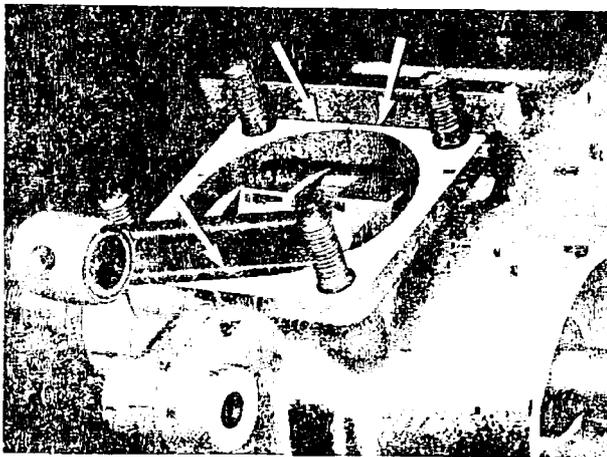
Der Pleuelschaft bzw. die Kurbelwelle müssen symmetrisch zur Gehäusetrennfuge liegen (unterer Pfeil). Die Flanschflächen beider Gehäusehälften dürfen nicht gegeneinander versetzt sein: prüfen mit Lineal (obere Pfeile)
